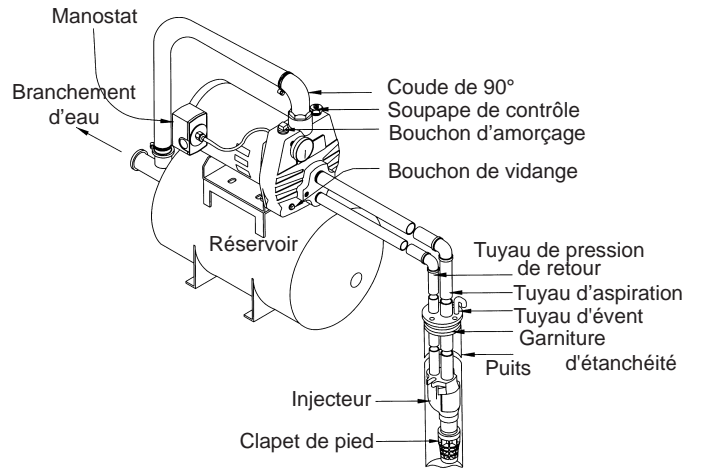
Puits peu profond - système monté sur le réservoir (installation à conduite double avec clapet de pied)
